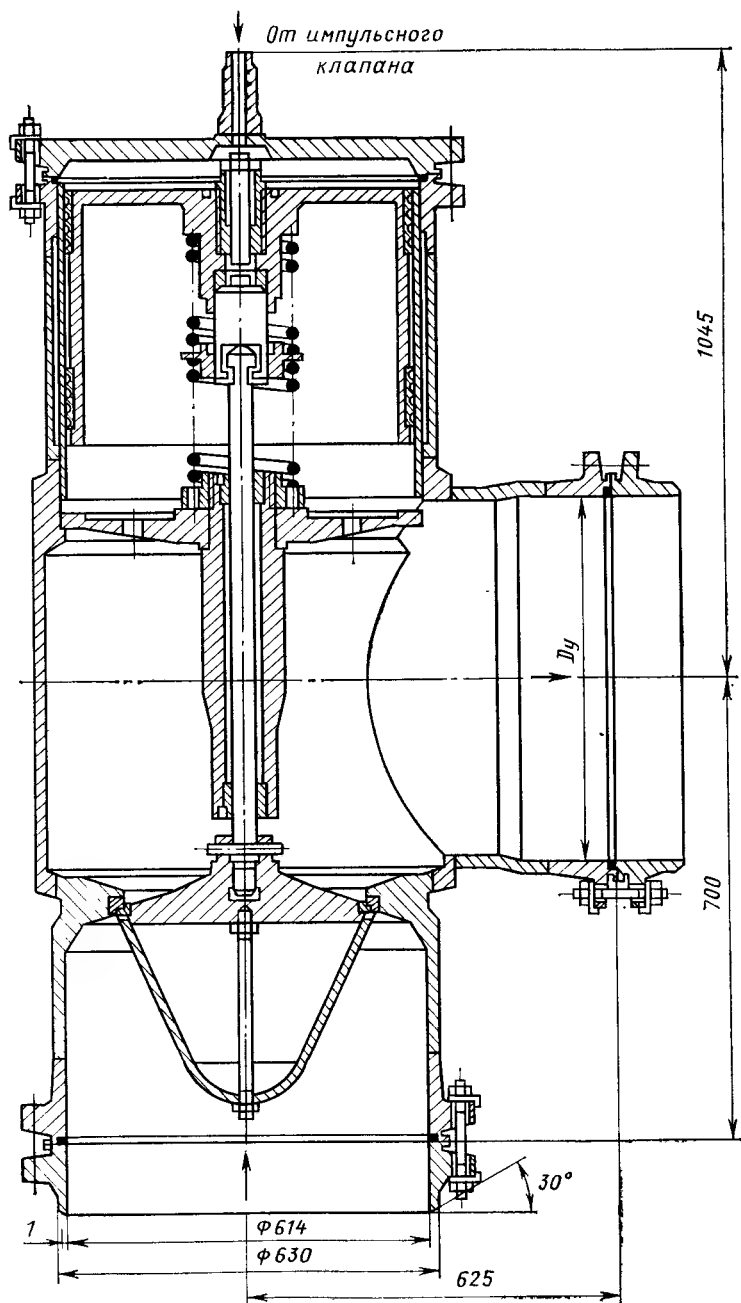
Предохранительный главный клапан Р 59015 на $p_p = 1,1$ МПа.
